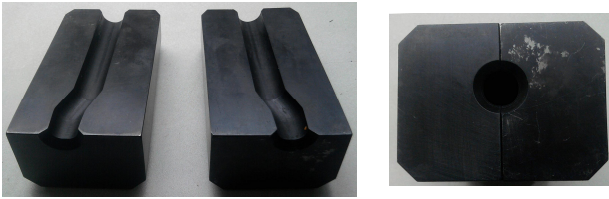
Общий вид матрицы для деформации ВЭ заготовок круглого сечения
